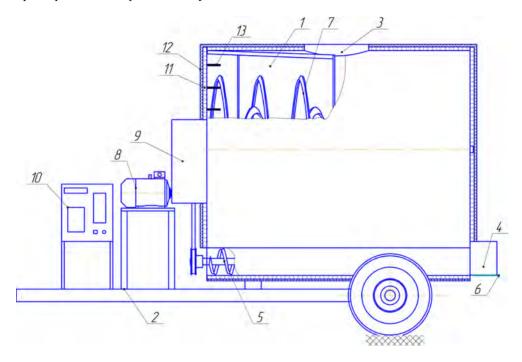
Смеситель-ферментер: 1 — бункер, 2 — рама; 3 — загрузочное окно; 4 — выгрузной патрубок; 5 — выгрузной шнек; 6 — заслонка, 7 — рабочий орган; 8 — электродвигатель; 9 — редуктор; 10 — пульт управления; 11 — нагревательный элемент; 12 — слой теплоизоляции; 13 — датчики температуры
